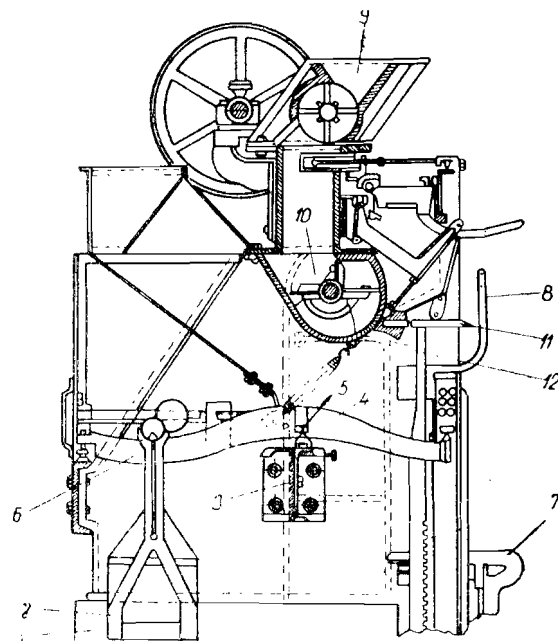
Balanță semiautomată pentru însăcuit ciment.
